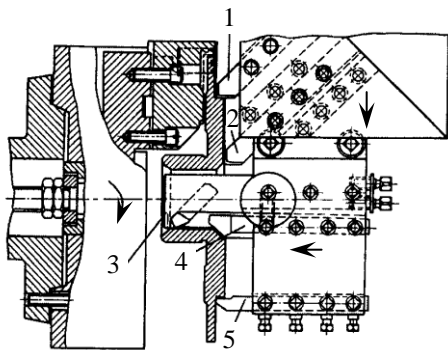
Налаштування багатерізевого напівавтомата для обробки кришки корпусу диференціала автомобіля
